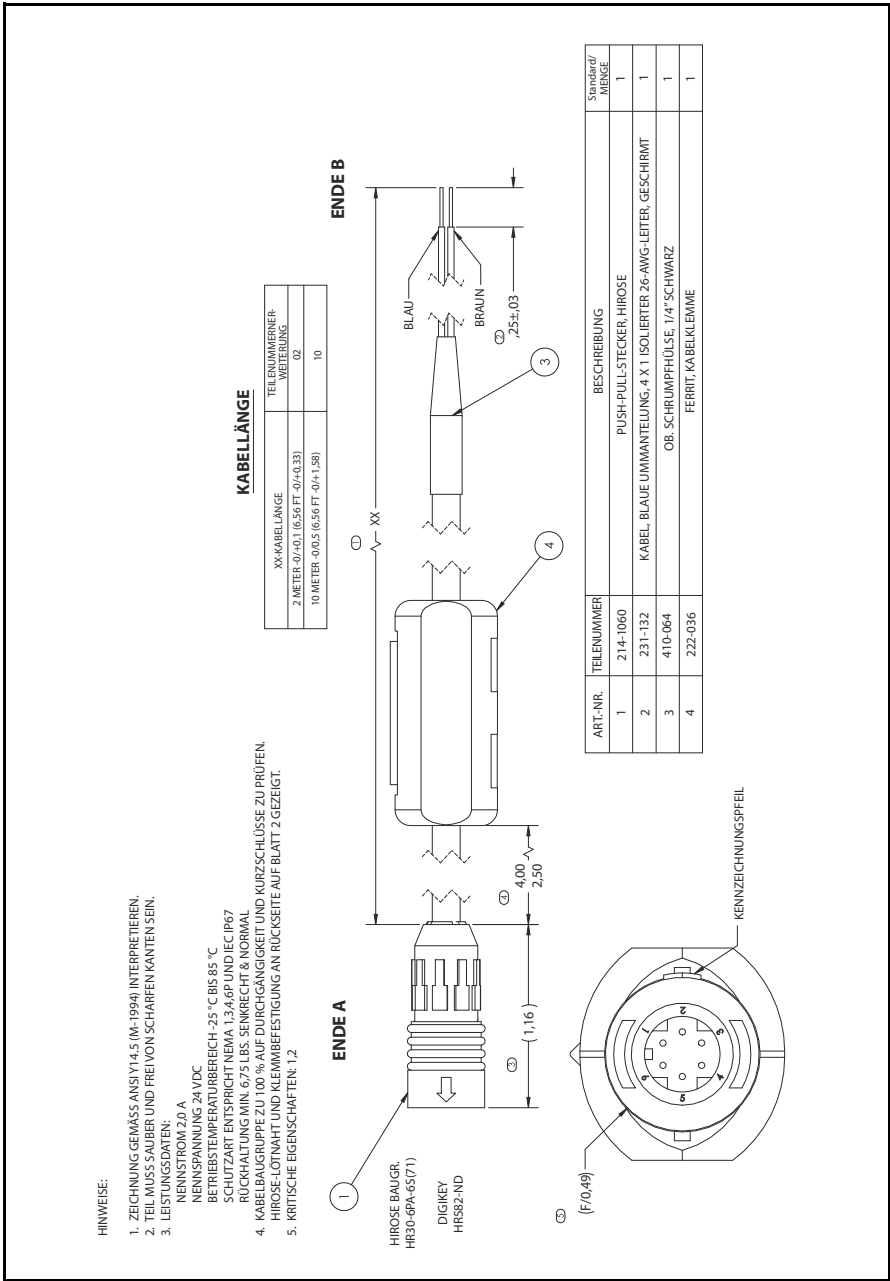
Kabel, IS (siehe Zeichnung 704-1318, Blatt 1 von 2)
